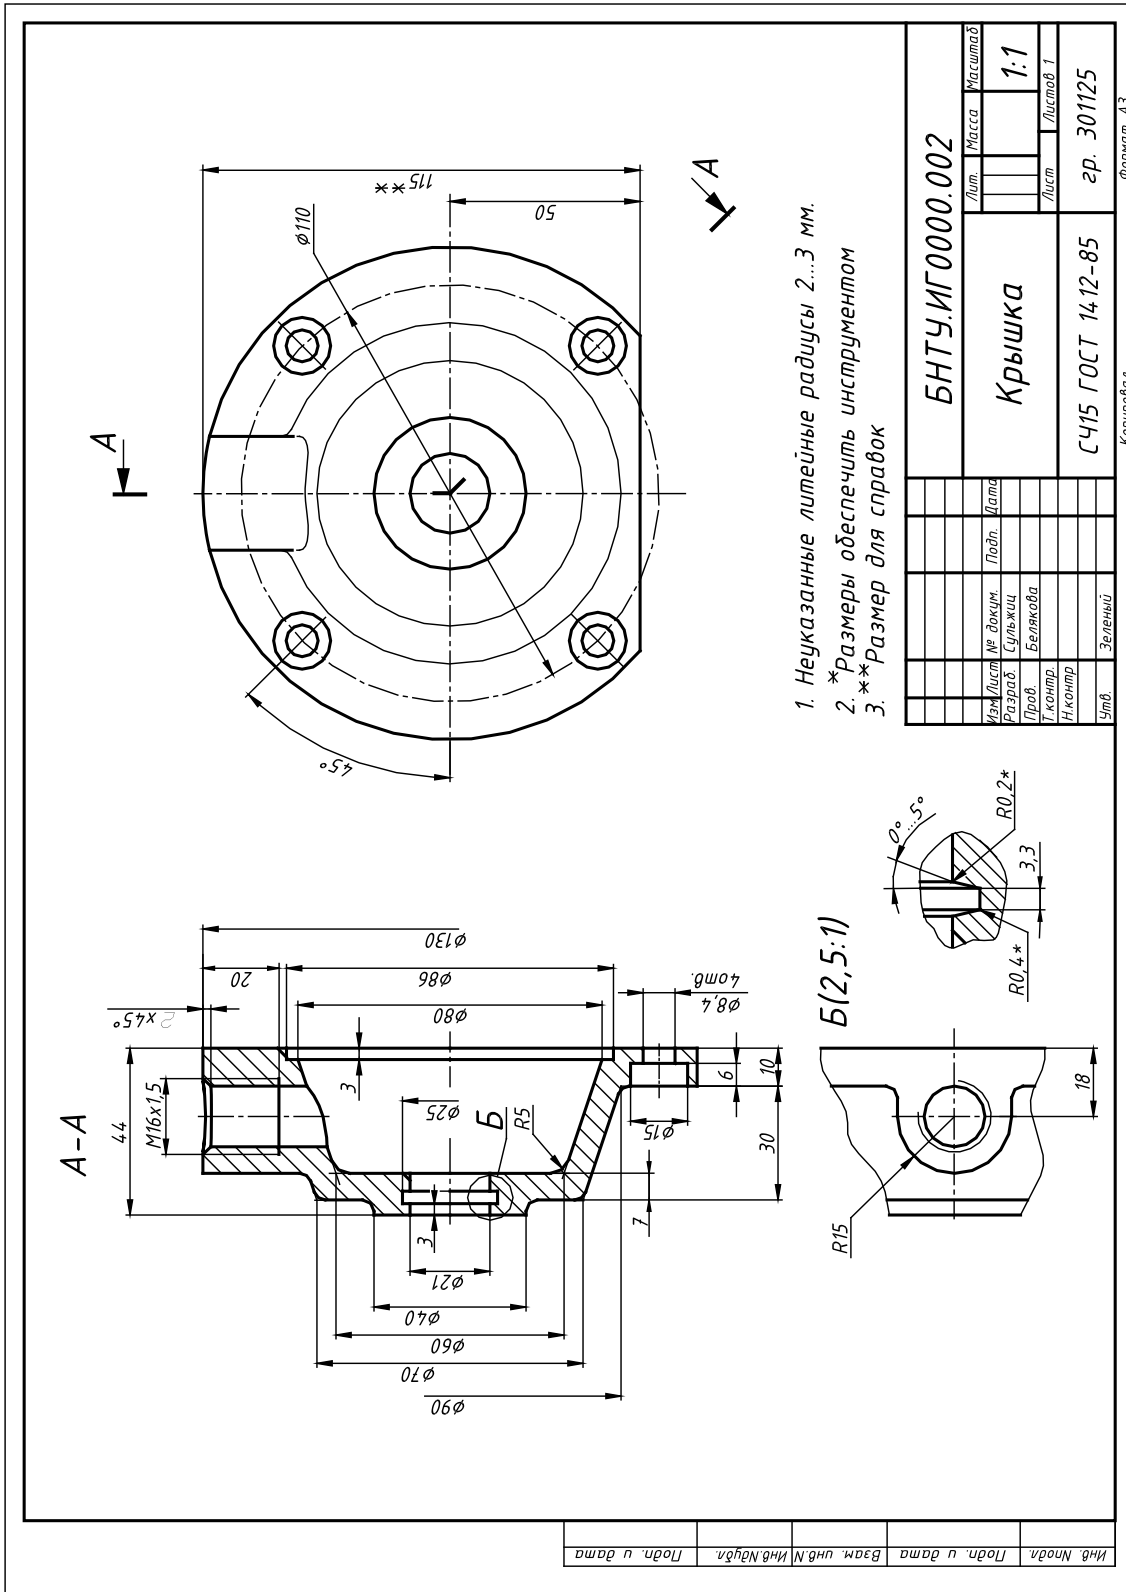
Чертеж крышки (выполнение ломаного разреза)
